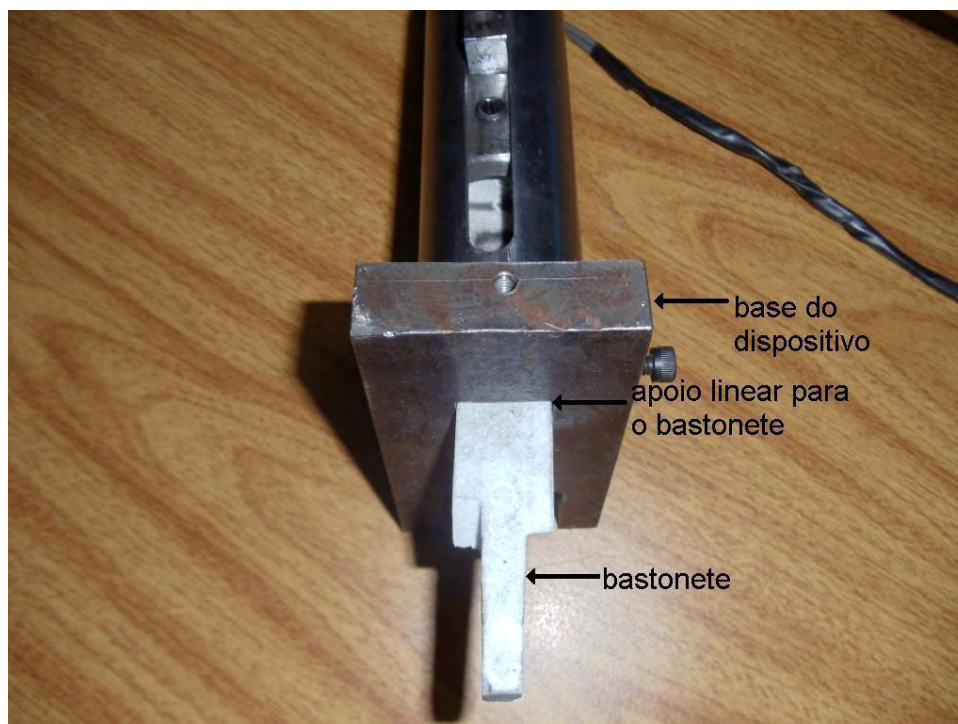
Estrutura do dispositivo de limpeza projetado.
